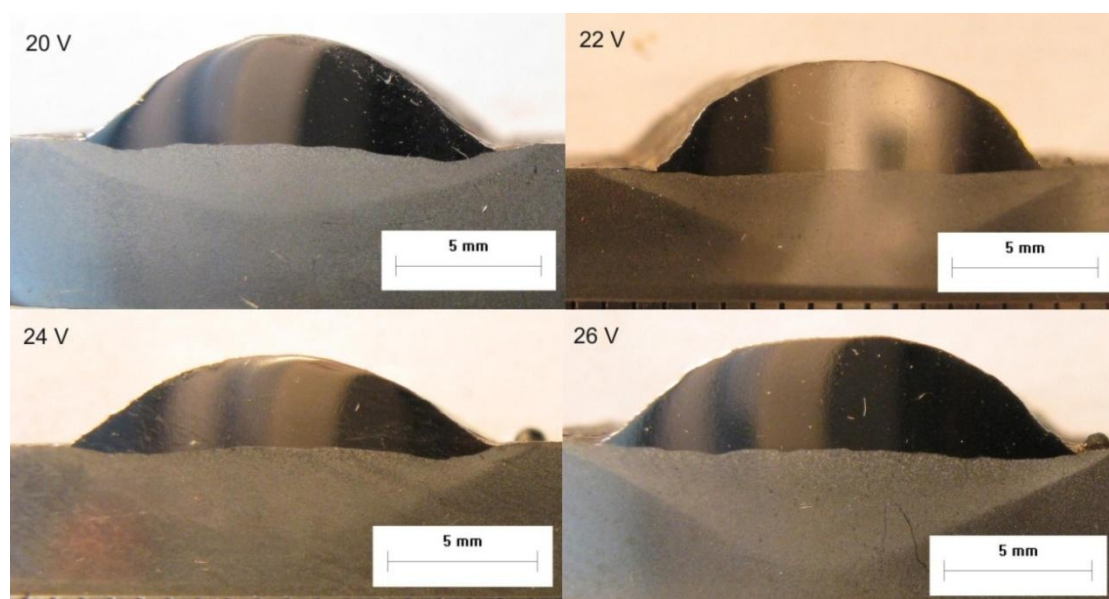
Geometria dos cordões de solda com tecimento triangular.
